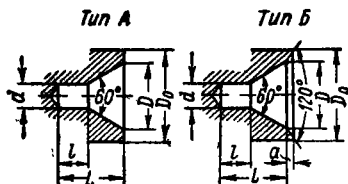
Формы центровых отверстий (размеры см. в табл. 96).
